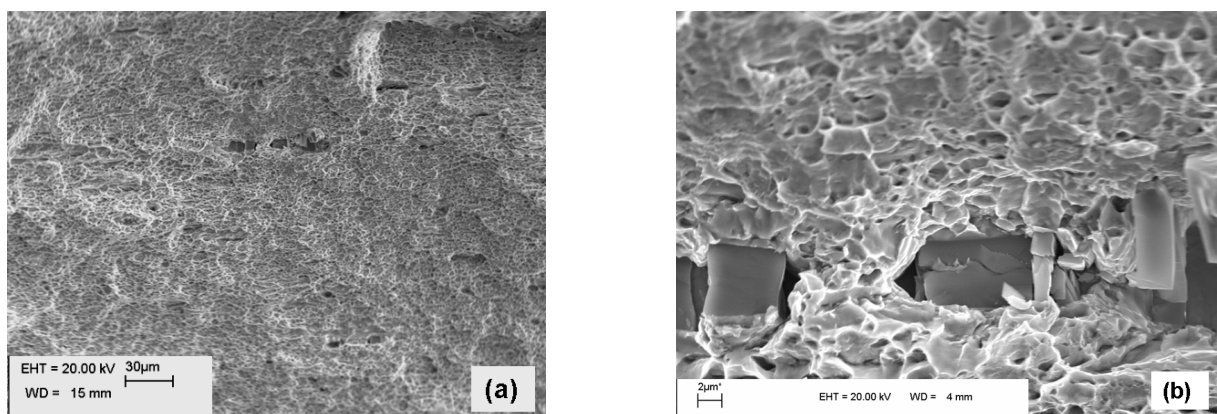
Fractographies acier CP (a) vue générale (b) zoom les inclusions
